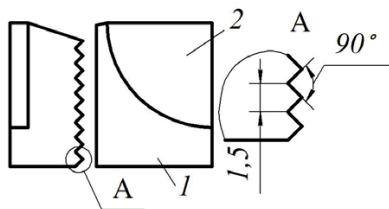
Нож с твердосплавной пластиной и форма рифлений на его поверхности: 1 – корпус ножа; 2 – пластина
